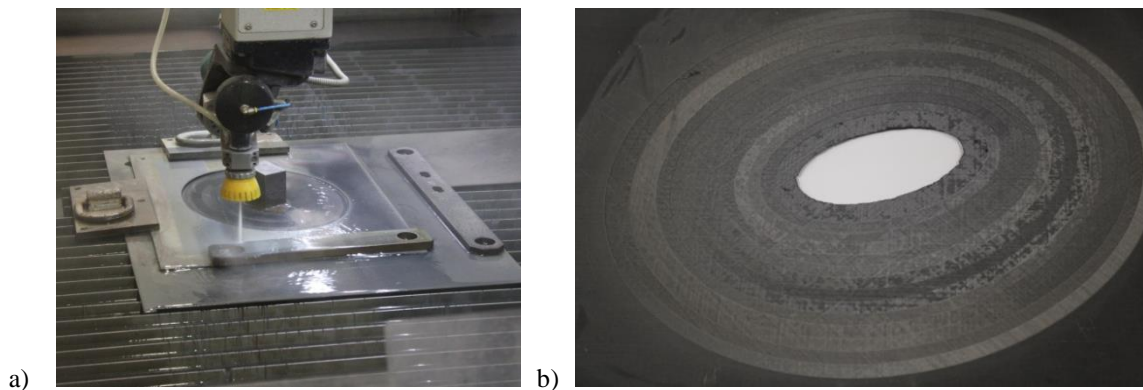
Enlèvement de matière par jet d'eau abrasif avec a) vue de l'évaluateur recouvert par les masques d'acier durant l'usinage et b) vue de la zone en escalier après usinage et ces quinze marches.
